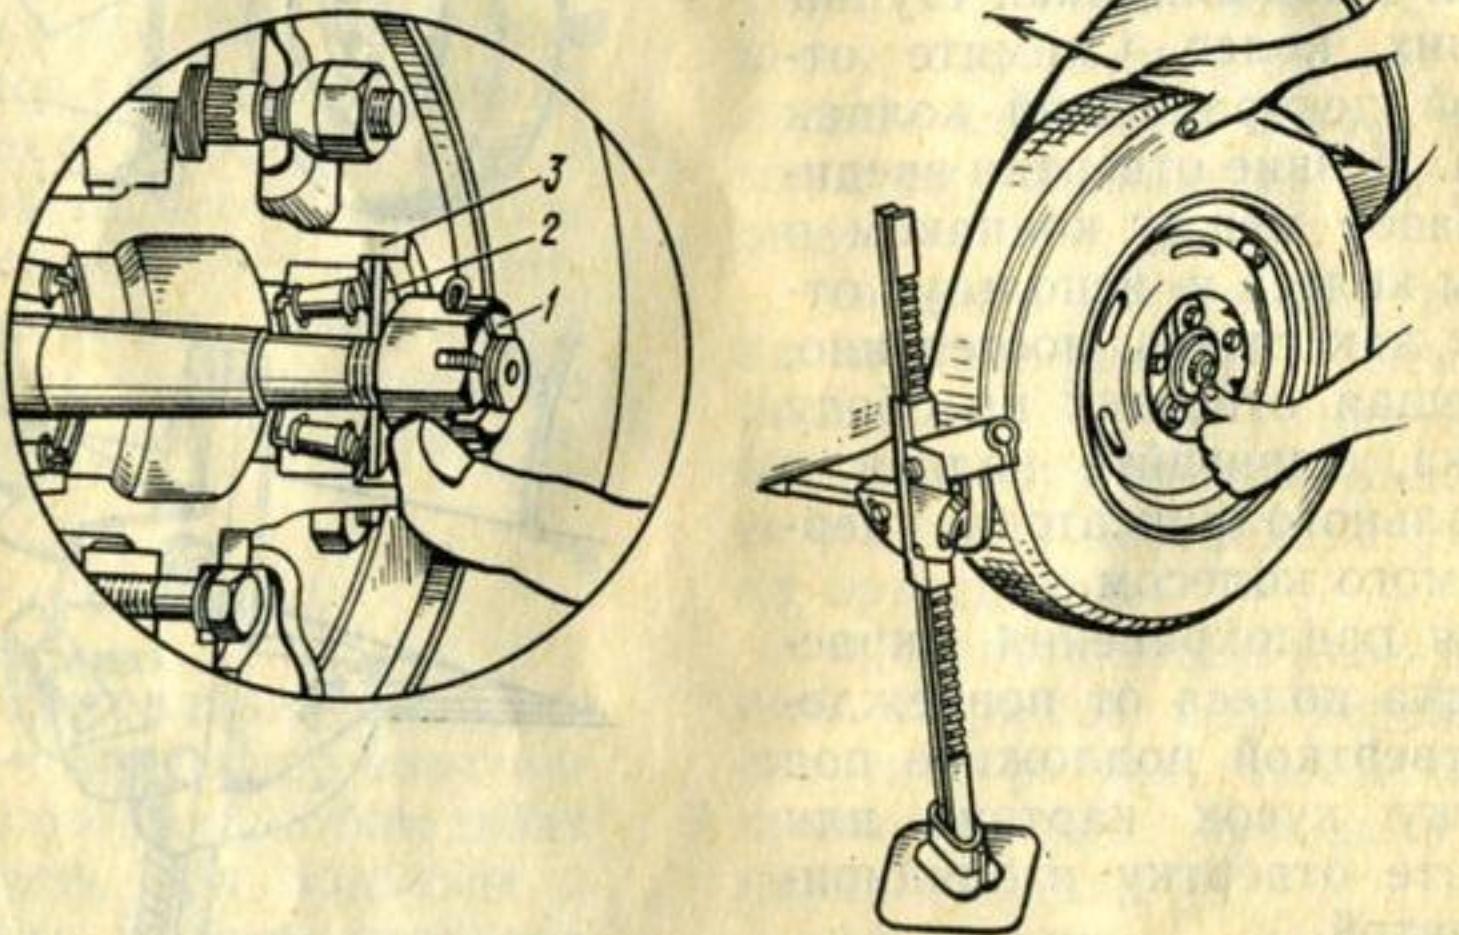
Проверка затяжки подшипников ступицы переднего колеса:
